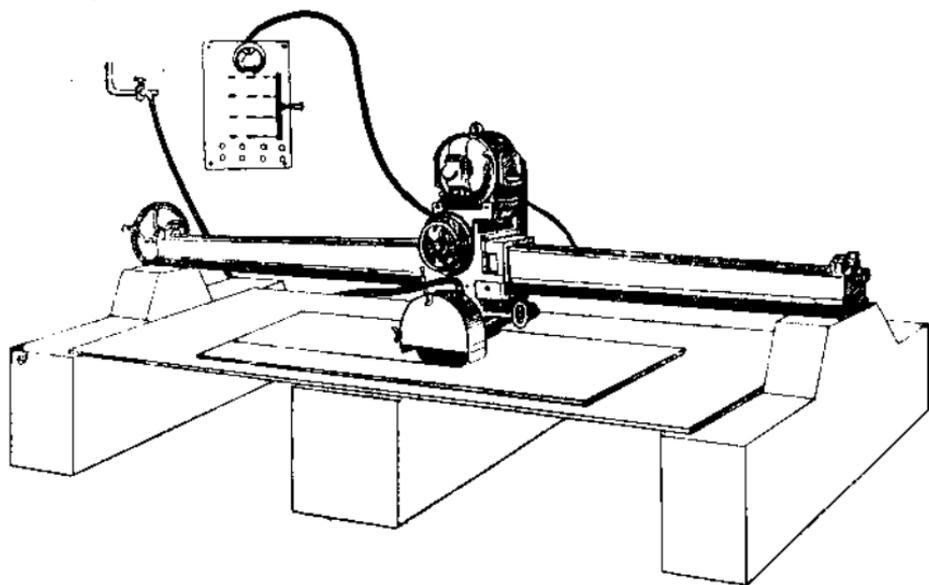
Фрезерный станок «Торпедо» с ручной подачей супорта
